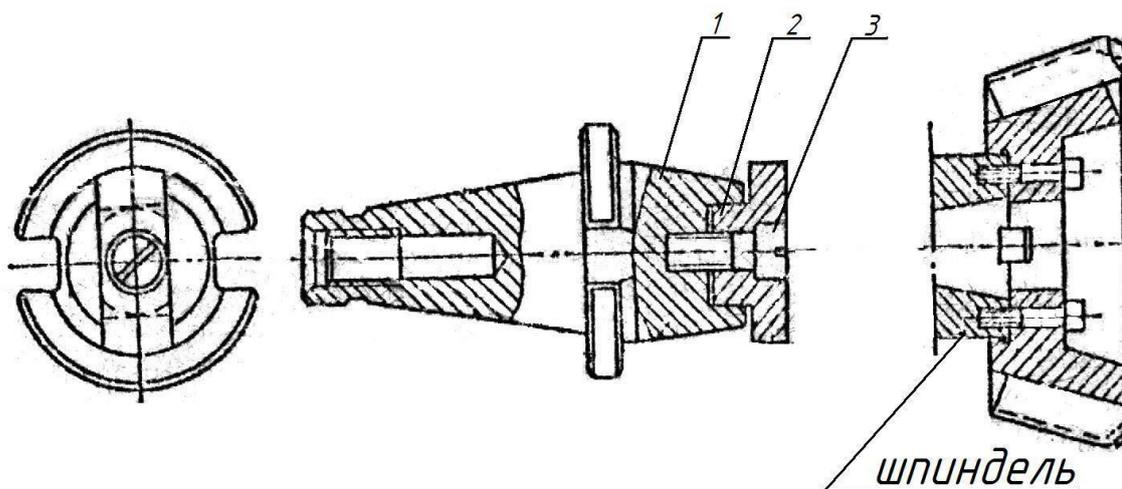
Крепление фрезерных головок: а-с коническим отверстием; б-с цилиндрическим отверстием.
